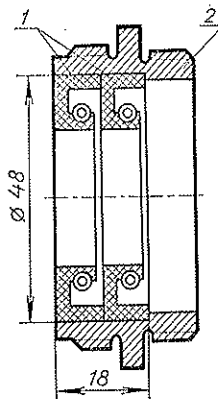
Модернизация гайки крепления подшипников ведущей шестерни:
